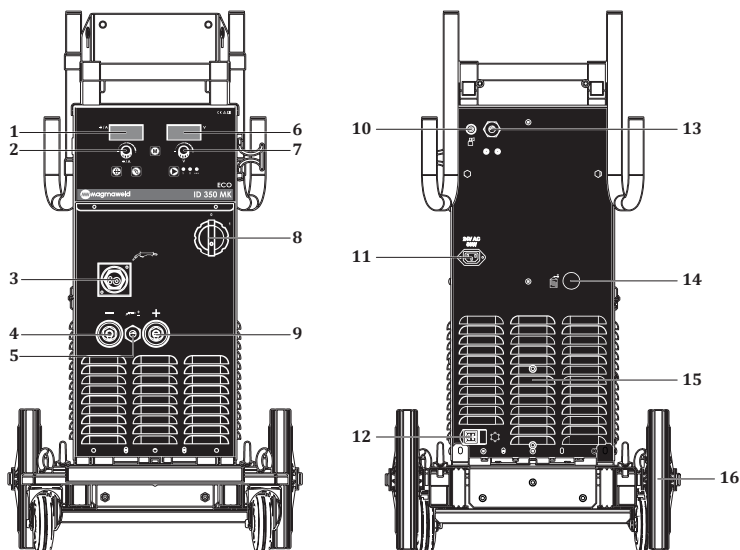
ID 250 - 350 MK ECO Vue Avant et Arrière
